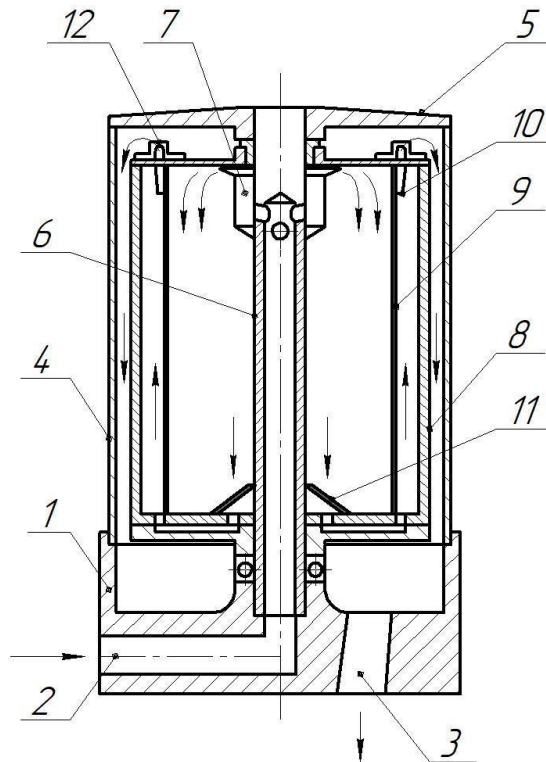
Сверхцентрифуга для очистки відпрацьованого моторного мастила: 1 – станина; 2 – канал для подачі мастила; 3 – канал для відведення масла; 4 – корпус; 5 – кришка; 6 – пола ось; 7 – розподільний стакан; 8 – ротор; 9 – перегородка; 10 – малий відбійний; 11 – великий відбійник; 12 – сопло
